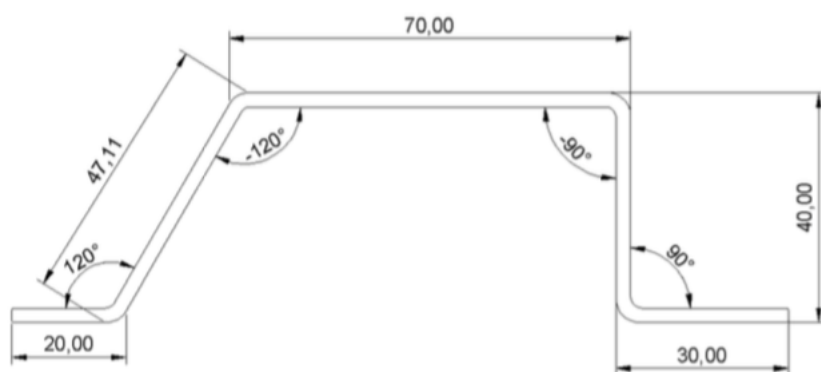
Пример рисуемой заготовки (внешние размеры)
